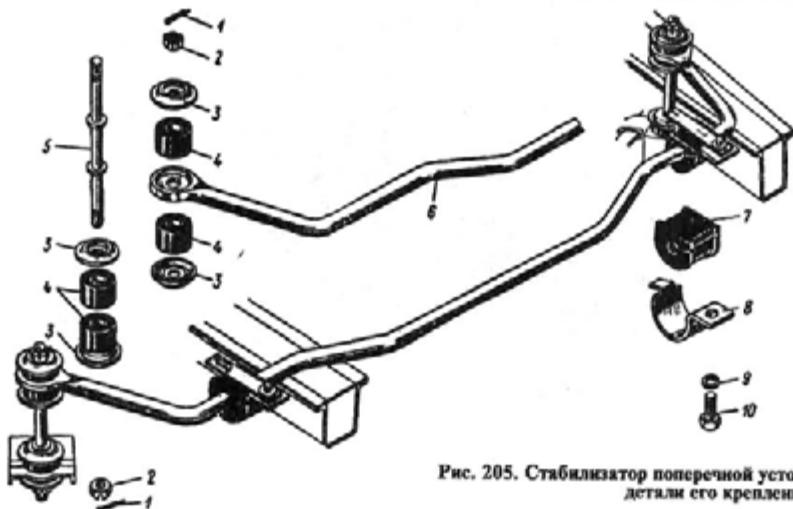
Стабилизатор поперечной устойчивости автомобиля и детали его крепления
